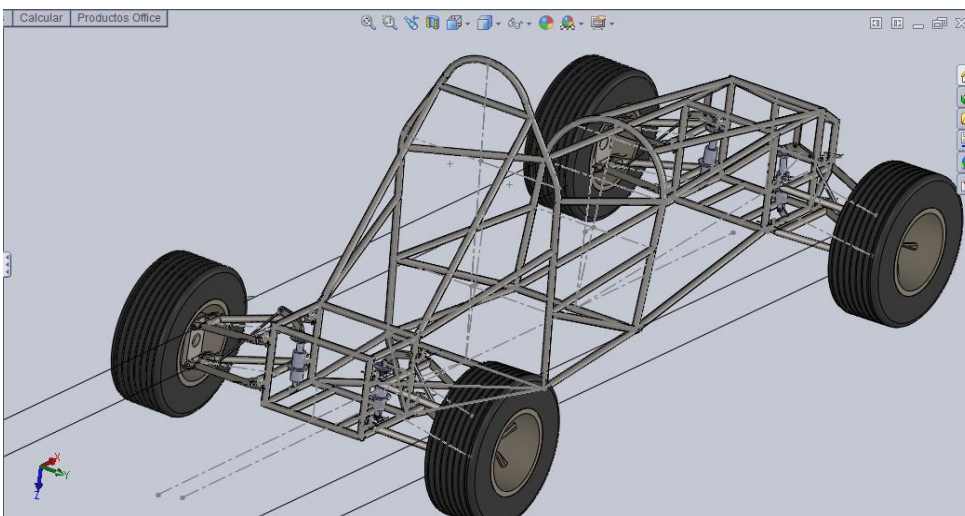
Vista isométrica de ensamblaje Push-rod
